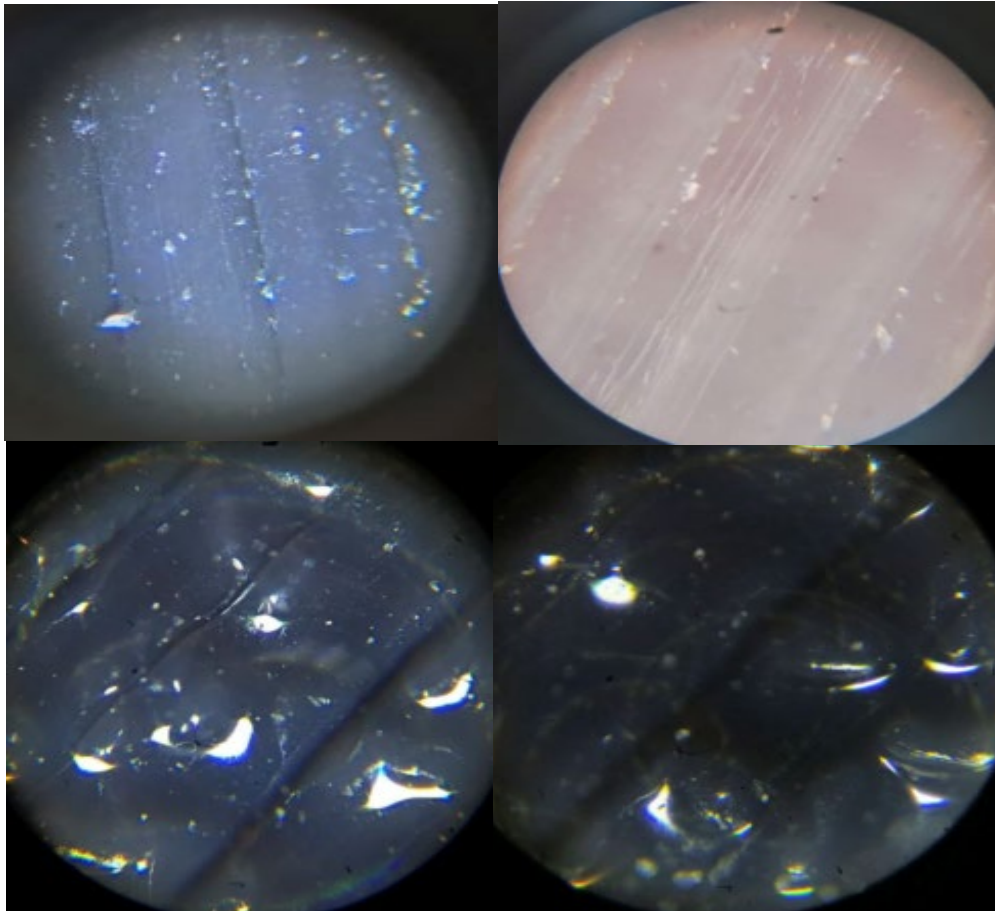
Схема дослідження деталі за допомогою мікроскопа: 1 – деталь корпусу підшипника; 2 – деталь валу; 3 – деталі бокової стінки робочої камери
